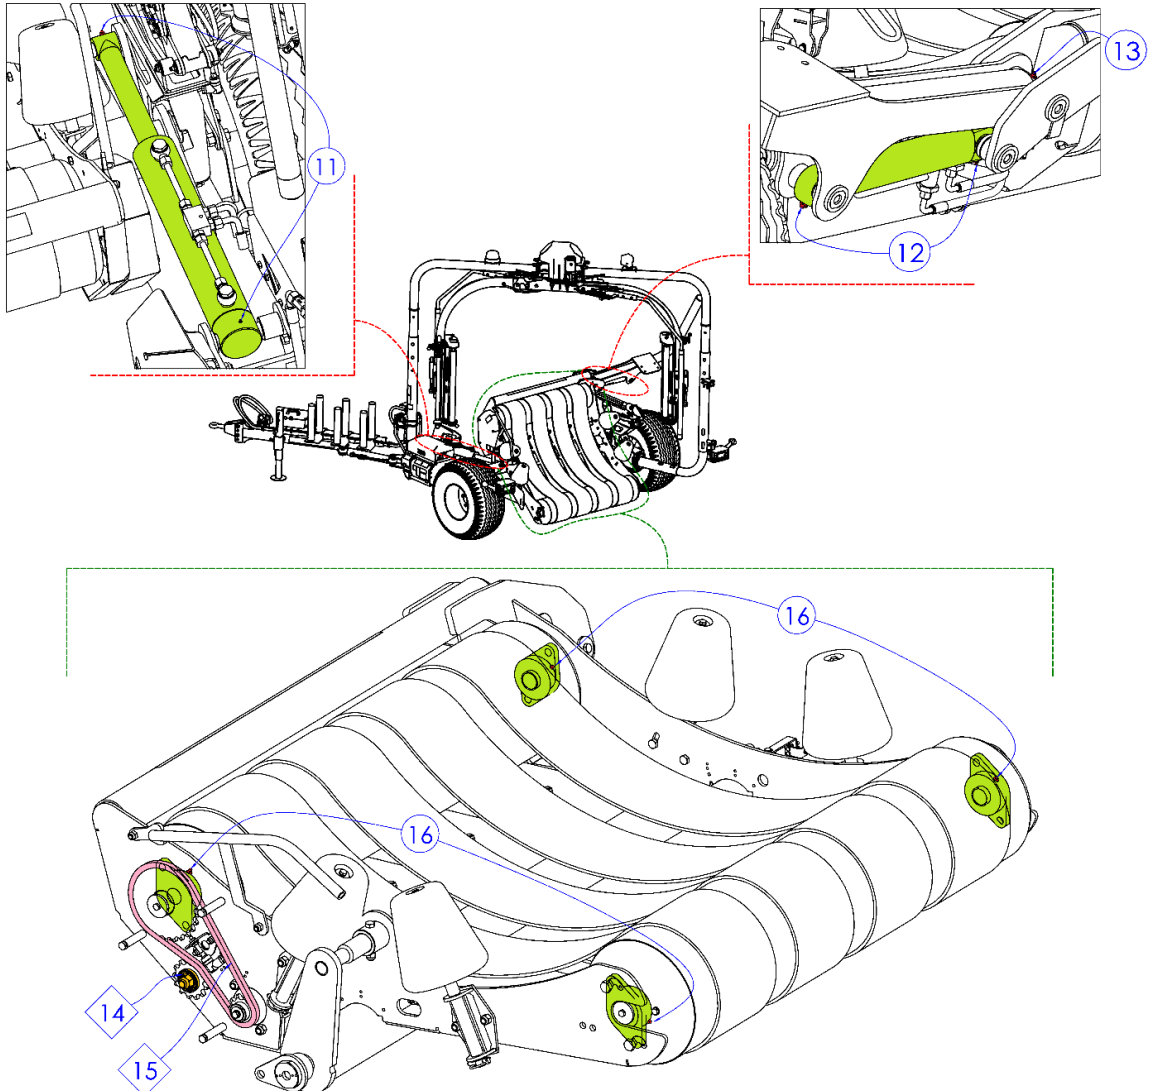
Точки смазки рабочего стола с погрузочной стрелой:
